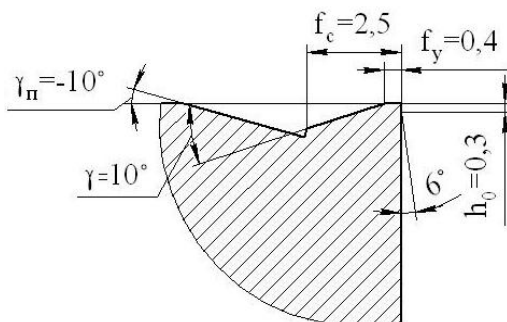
Форма режущей пластины с упрочняющей и стабилизирующей фасками по передней поверхности и с предварительным притуплением по задней.
